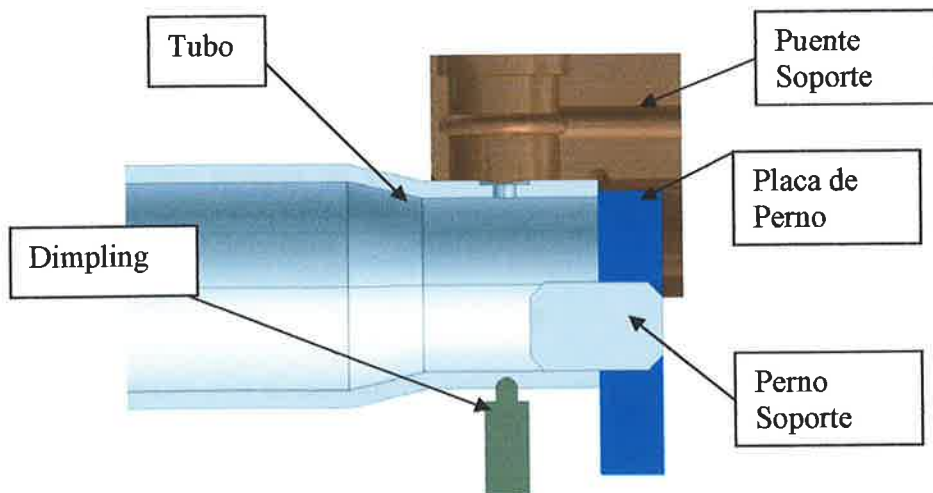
Partes principales seccionadas que componen el proceso dimpling.
